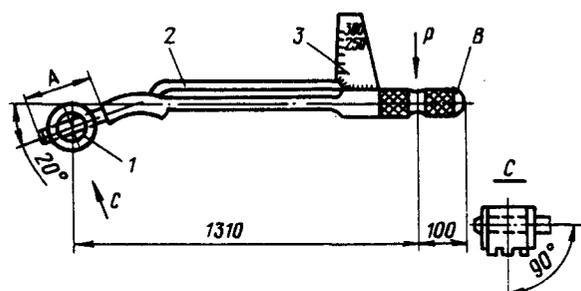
Тарированный ключ для затяжки и гайки крепления втулки несущего винта:
